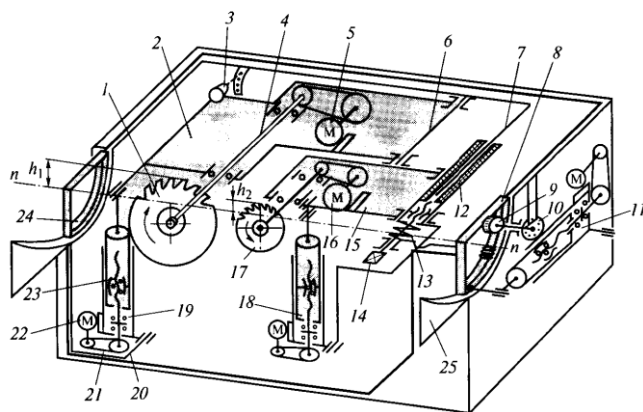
Кінематична схема пильного агрегату: 1 – основна пилка; 2 – платформа; 3 – датчик виступу пилки; 4 – вал; 5, 16 – електродвигуни; 6, 7 – осі; 8, 24 – сектори; 9 – шестерня; 10 – датчик нахилу пилок; 11, 18, 19 – механізми позиціонування; 12 – гільза; 13 – пружина; 14 – гвинт; 15 – плита; 17 – підрізна пилка; 20 – корпус агрегату; 21 – зубчастий ремінь; 22 – електродвигун механізму позиціонування; 23 – гвинтова передача; 25 – напрямна станини
